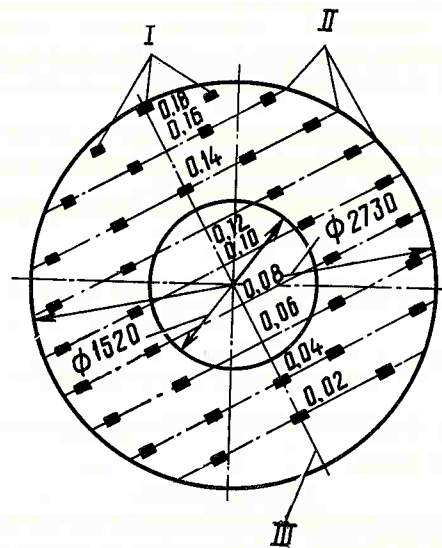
Разметка мест нанесения маяков для шлифовки клиновидного слоя зеркального диска: I — глубина маяков; II — линия маяков; III — плоскость биения
